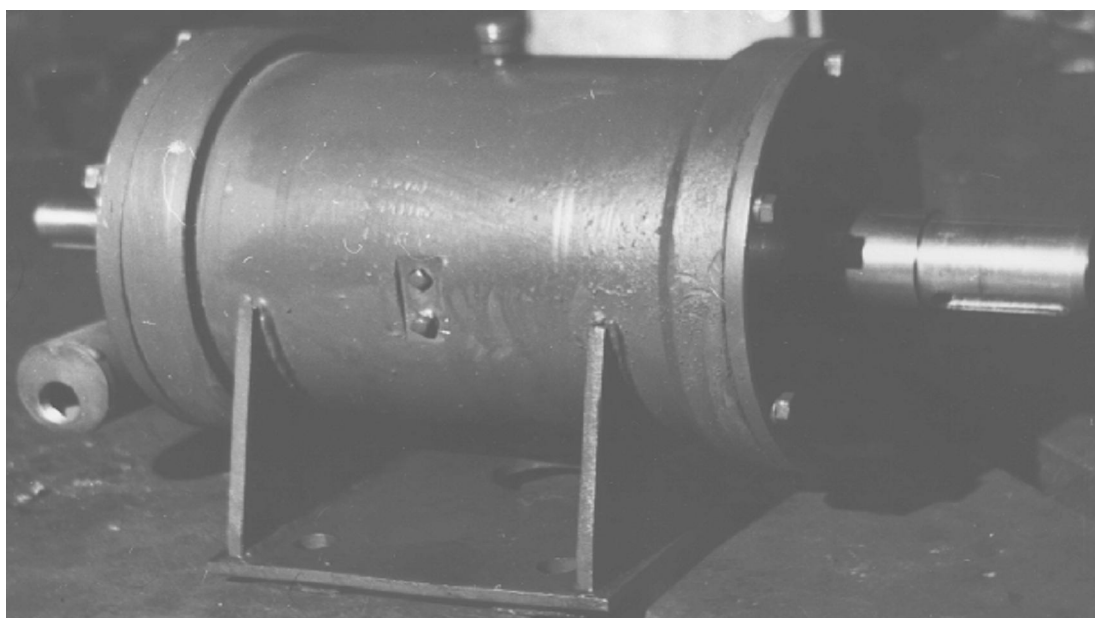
Редуктор с промежуточными телами качения ПТК – 165 в сборе:
